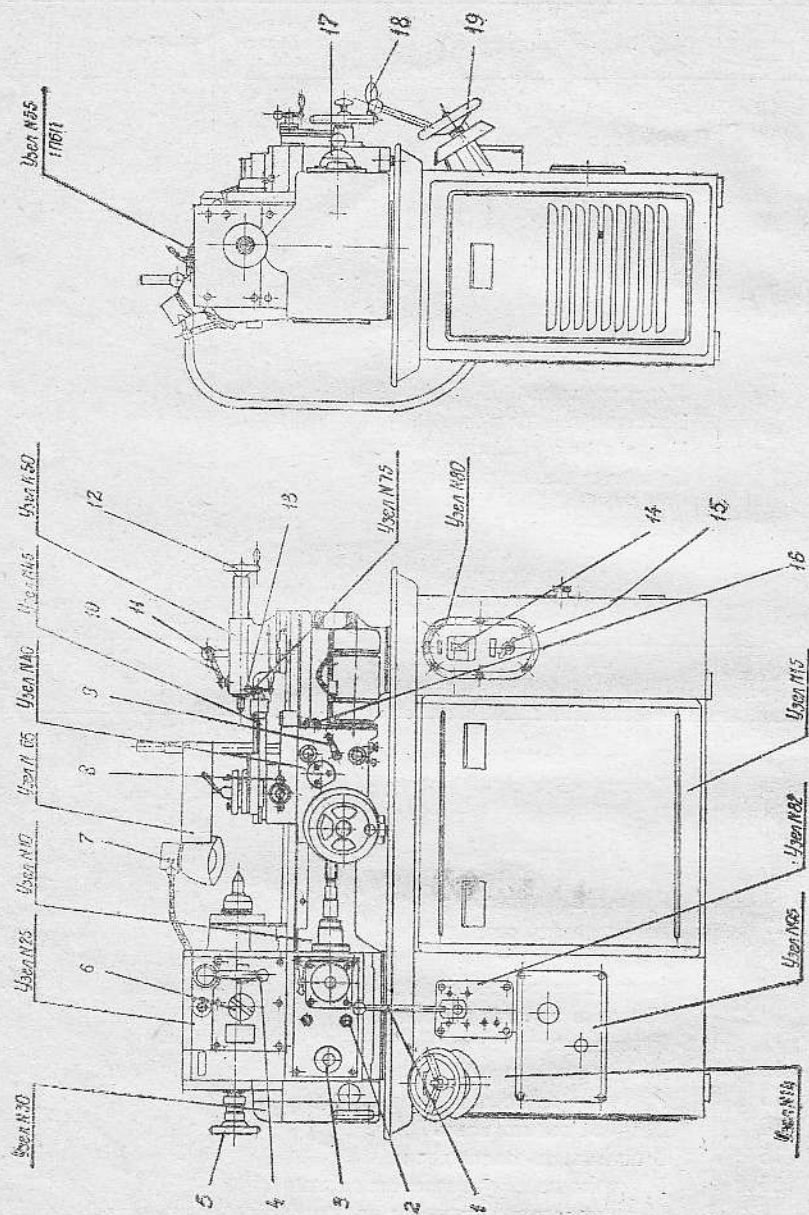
Общий вид станка (с обозначением узлов и органов управления).
